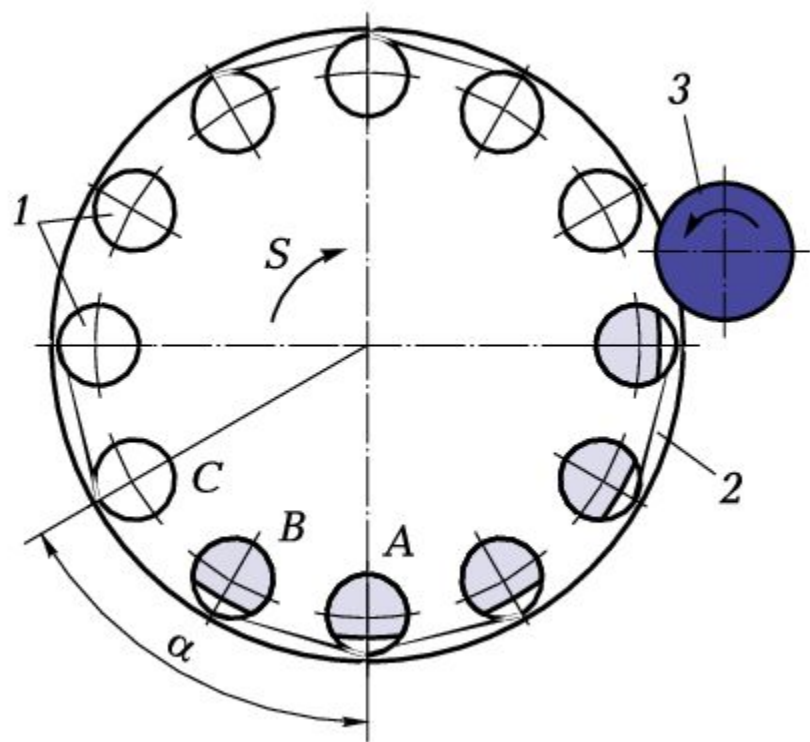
Схема одновременной непрерывной обработки заготовки:
